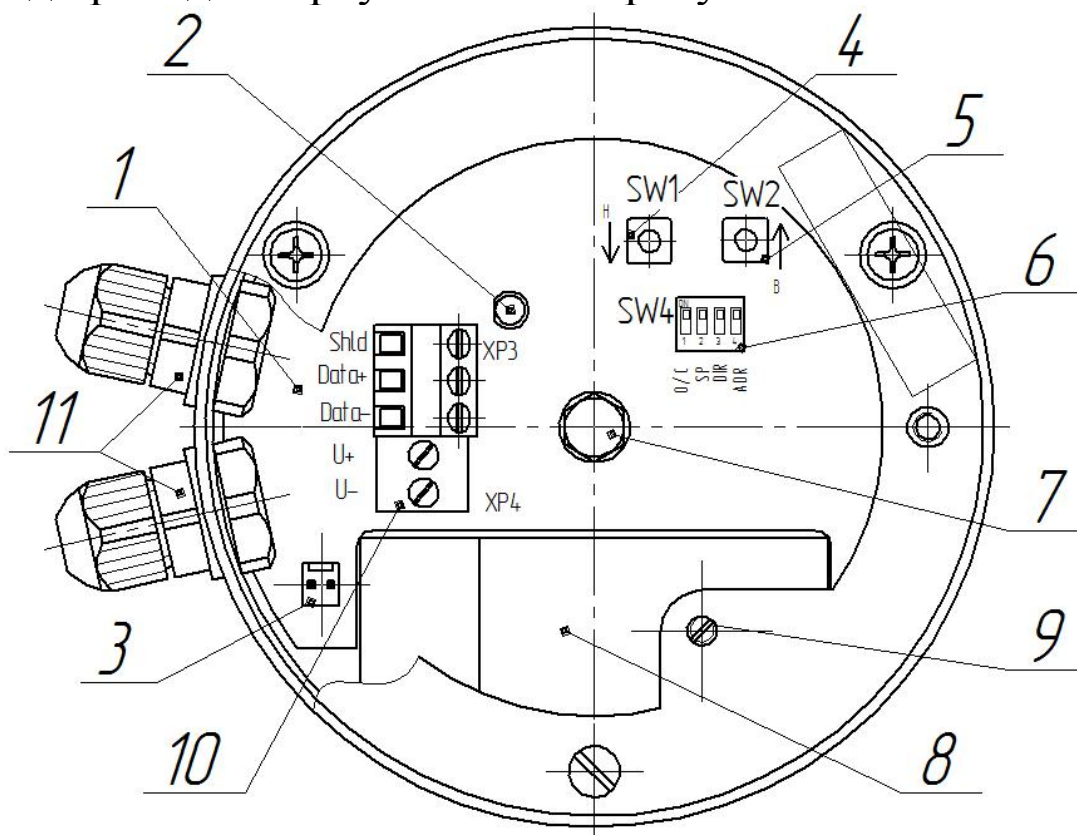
Вид привода ЭП-200 сверху без крышки
